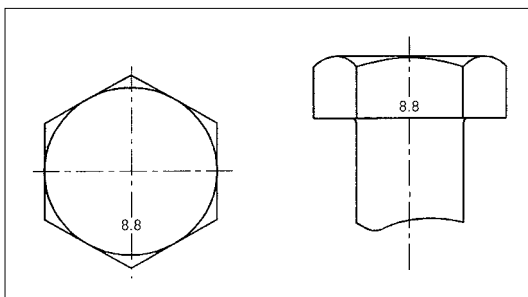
Abb. G: Beispiel für die Kennzeichnung von Sechskantschrauben
